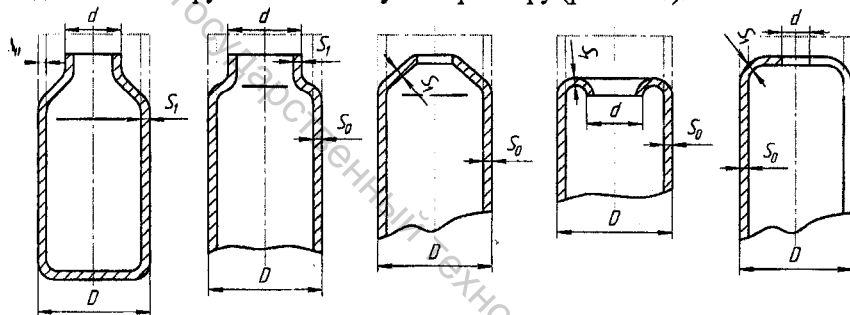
Конструктивные варианты обжима заготовки
